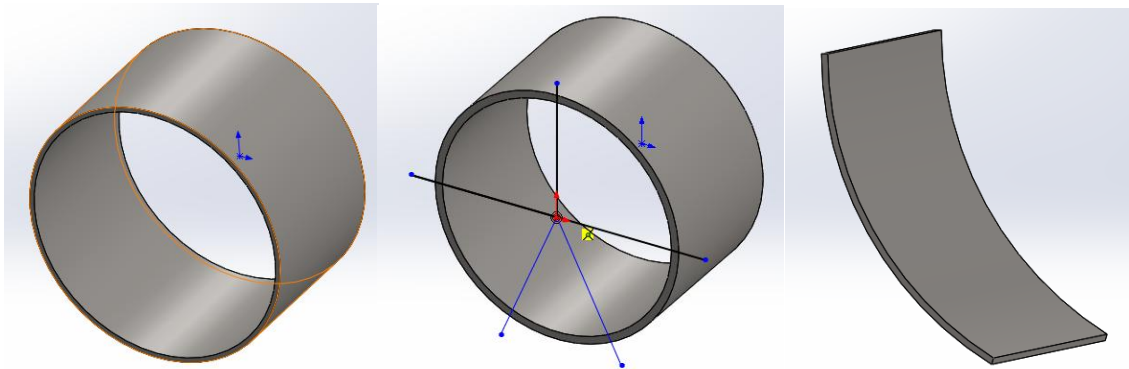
Cuerpo dentado Imagen 75: Cuerpo dentado marcado Imagen 76: Pieza cortada
